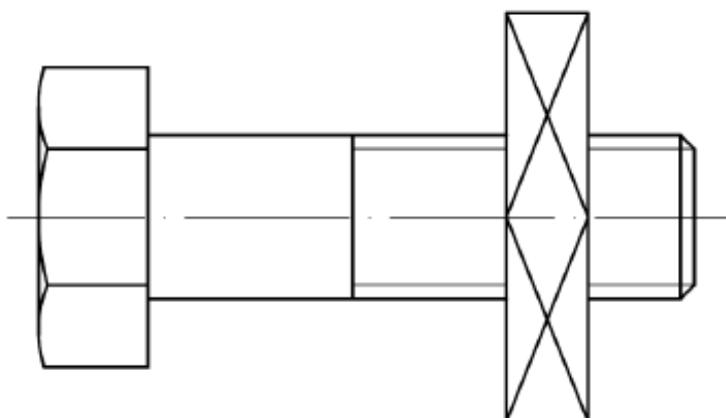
Zobrazenie šesthranných skrutiek a matíc
